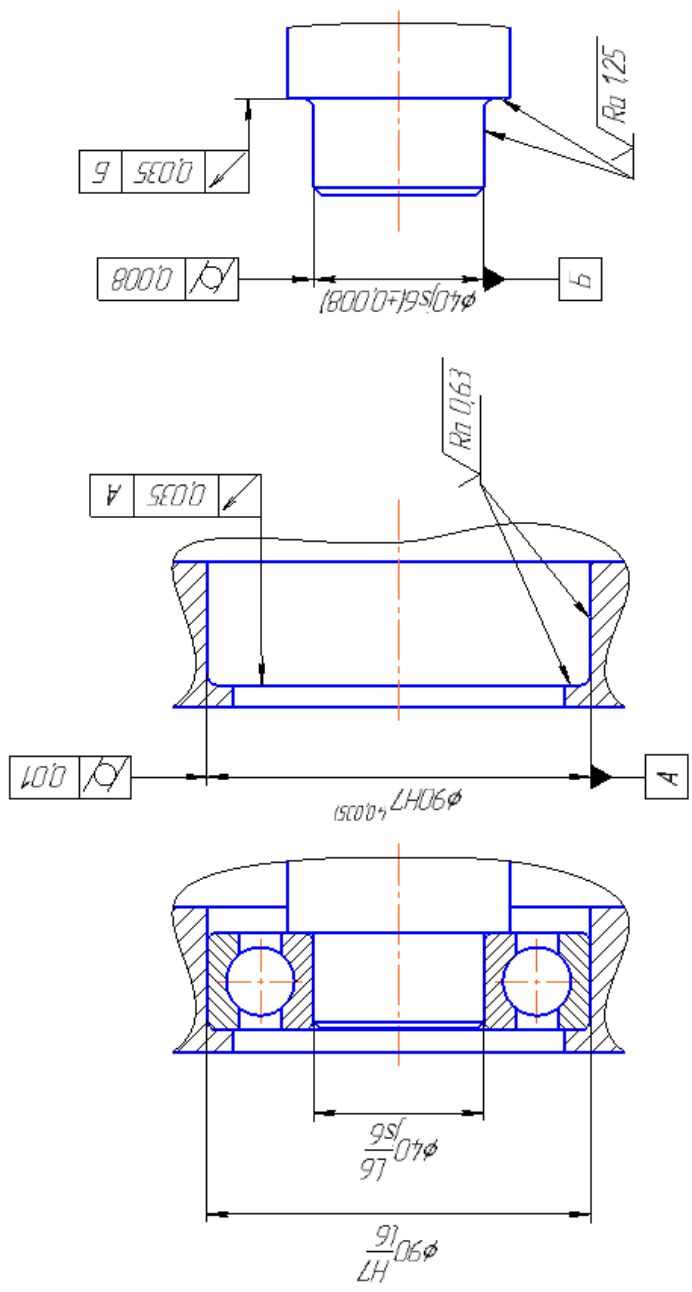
Эскизы соединения с подшипником вала и корпуса
